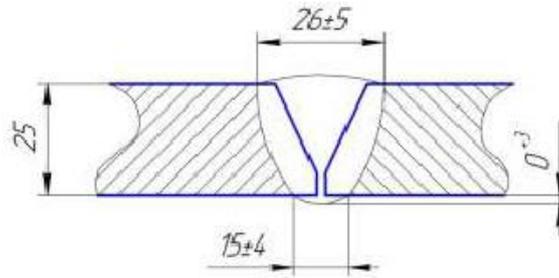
Конструктивные размеры сварного шва
